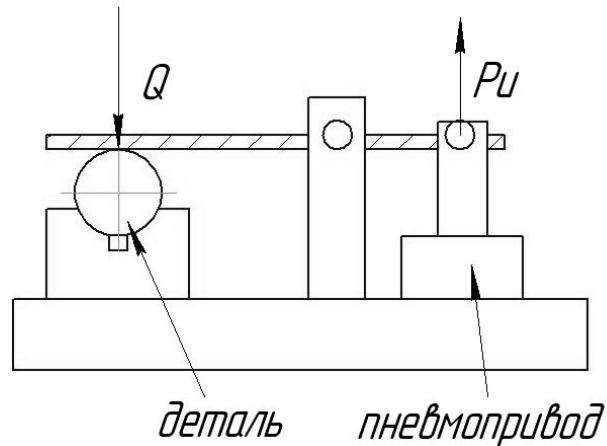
Розрахункова схема сил закріплення заготовки
